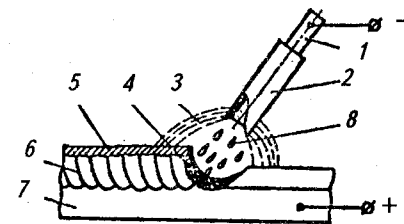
Ручная дуговая сварка металлическим электродом с покрытием (стрелка указывает направление сварки): 1 — электрод; 2 — покрытие электрода; 3 — газовая защита вокруг дуги; 4 — сварочная ванна; 5 — шлаковая корка; 6 — шов; 7 — основной металл; 8 — капли жидкого металла
